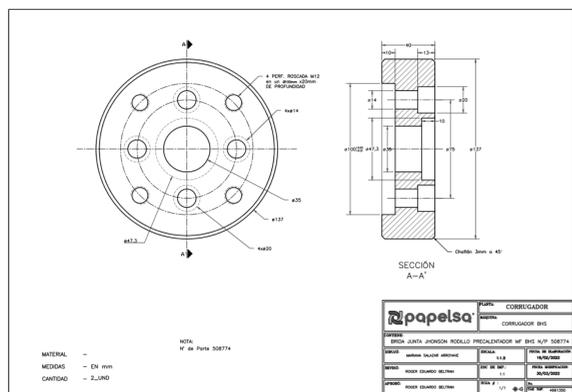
Plano BRIDA JUNTA JHONSON RODILLO PRECALENTADOR MF BHS N/P 508774
